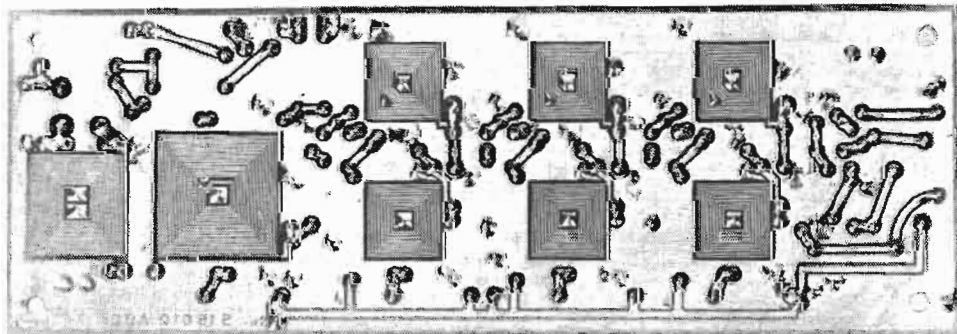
On distingue fort bien, sur cette photographie, les bobinages imprimés
